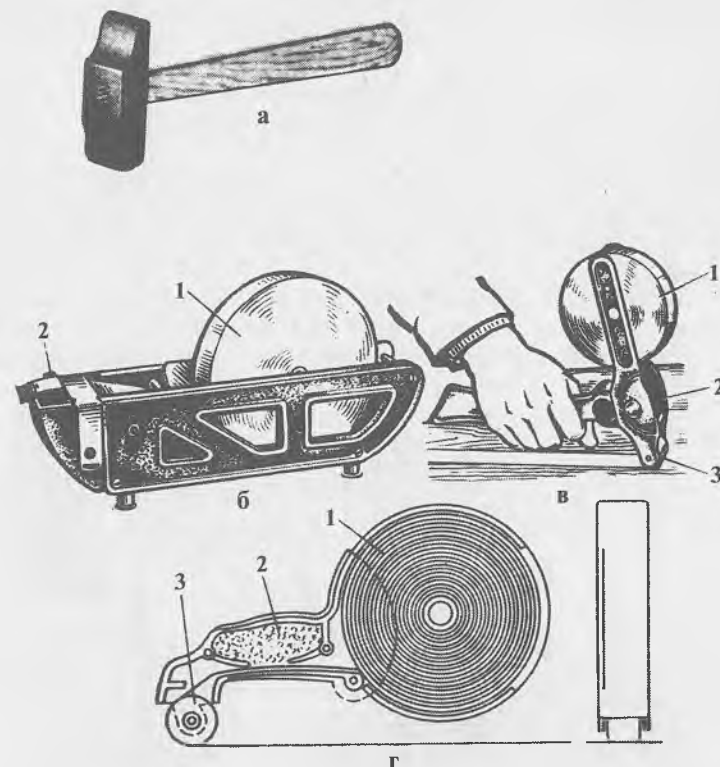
Инструменты и приспособления для наклеивания клеевой ленты:
